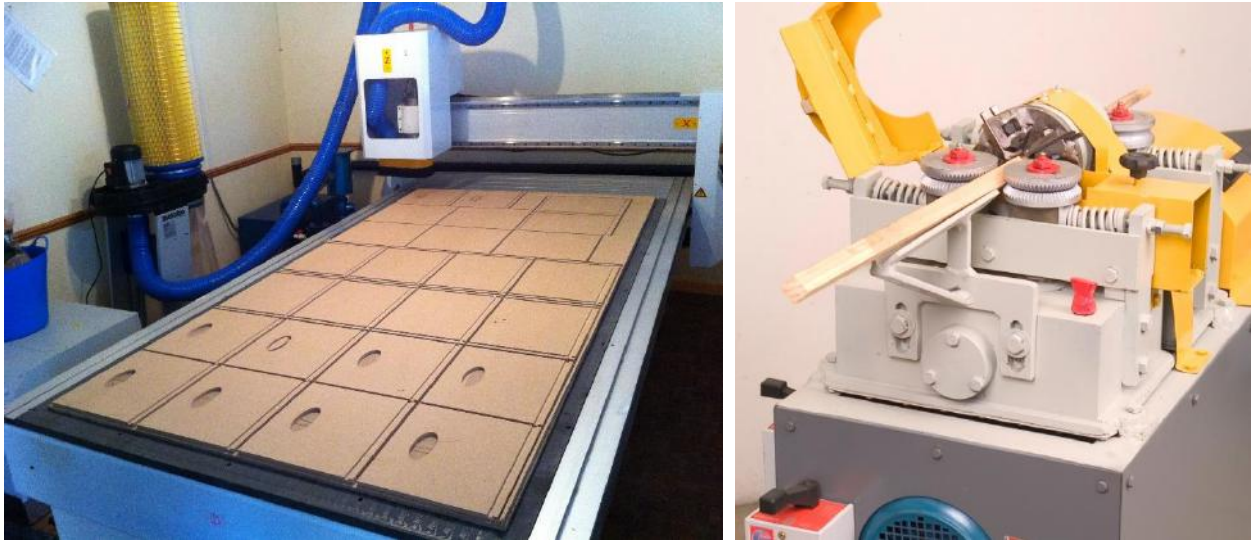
Fresa CNC e Torno Tubular. Fonte (Fresa CNC) www.cleancutwood.com; (Torno Tubular) www.maquinasagua.com.br.
